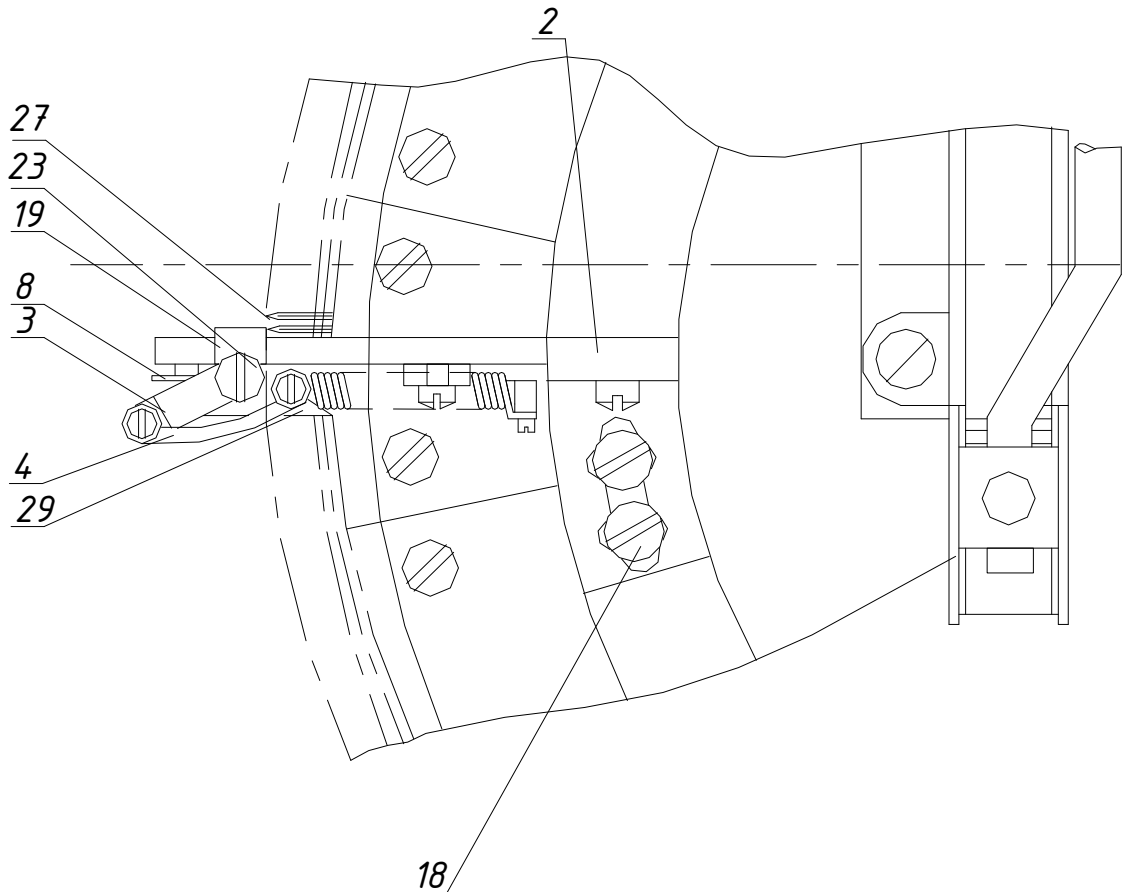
Механізм для котельних машин для автоматичного розрізання нитки, вид зверху
